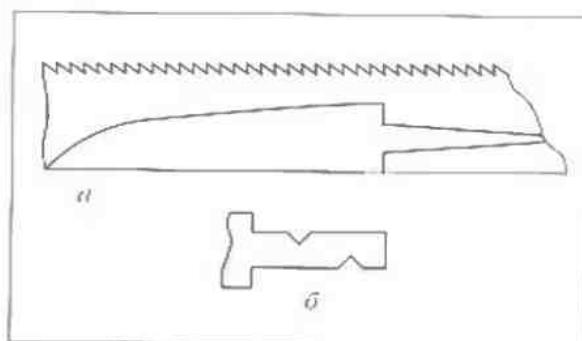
Схема изготовления ножа из полотна механической ножовки по металлу (а) и вариант хвостовика (б) (масштаб 1:2)
